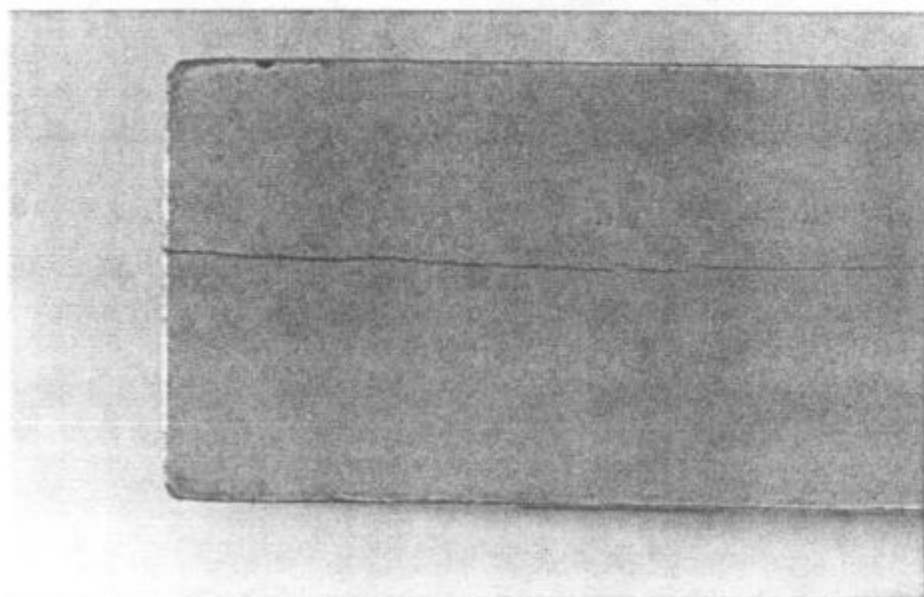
Extremo de fisura en la cara lateral de la probeta. Parte más abierta de la fisura. Zona G del caño. 7X.
